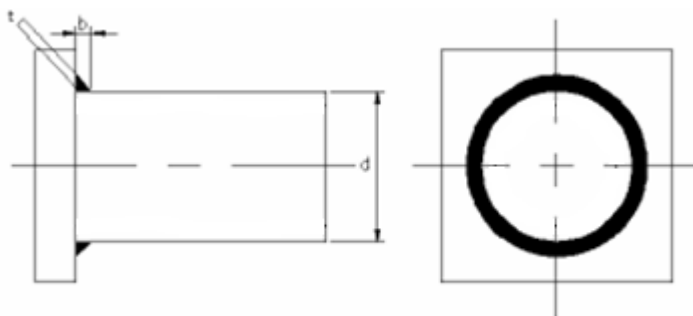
Dimensionamiento de soldadura en Eje
